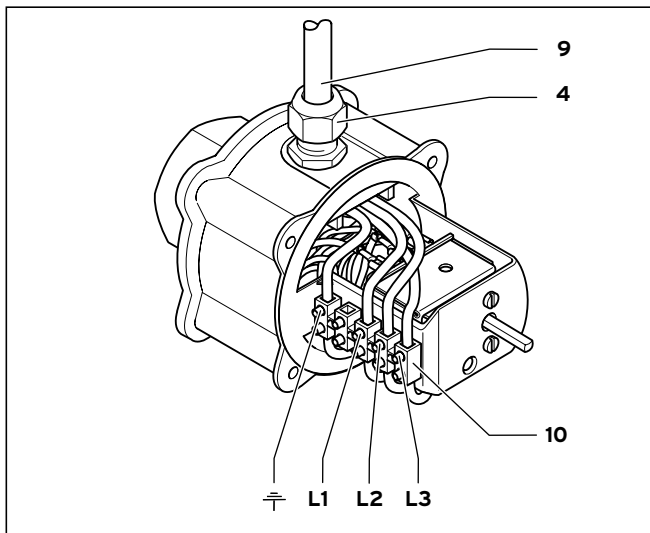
Installazione elettrica Riscaldatore ad immersione su tappo filettato da 400 V
